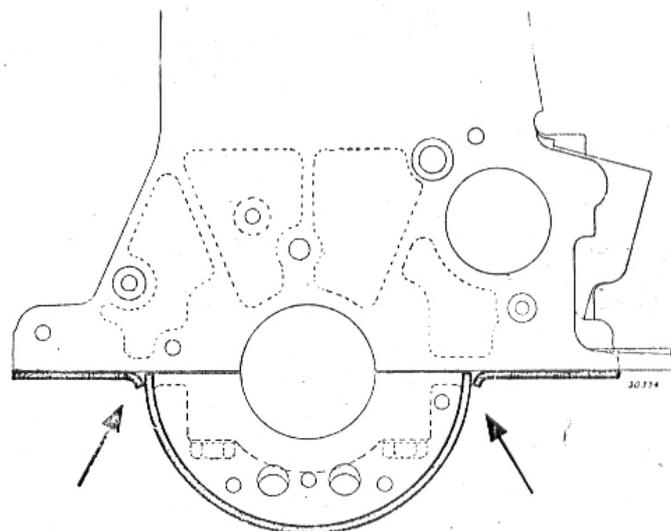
MONTAGE DES JOINTS DU CARTER D'HUILE.
